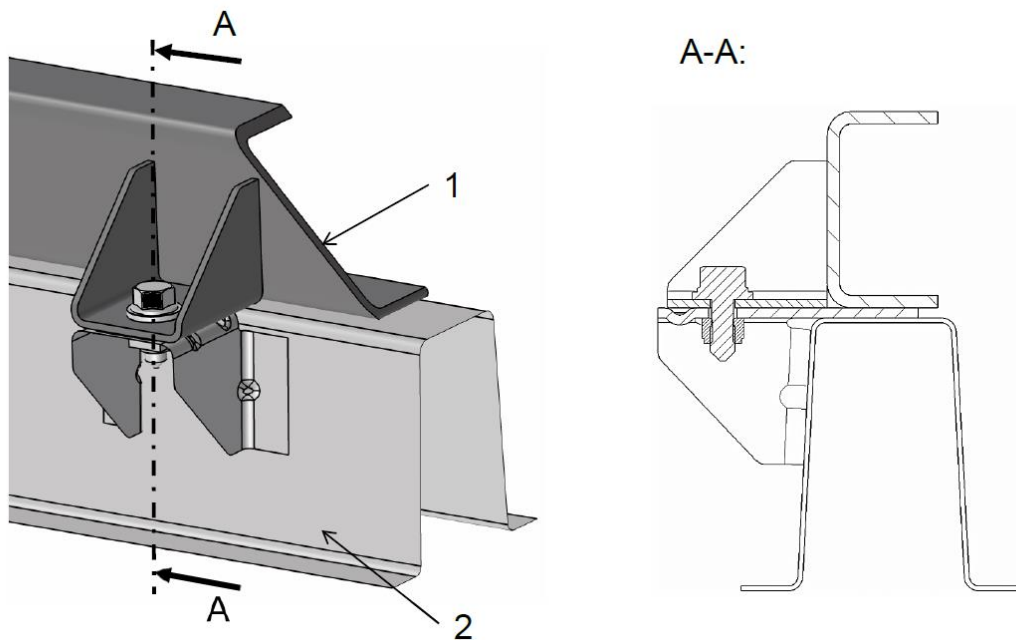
Befestigung des Hilfsrahmens am Fahrzeugrahmen
